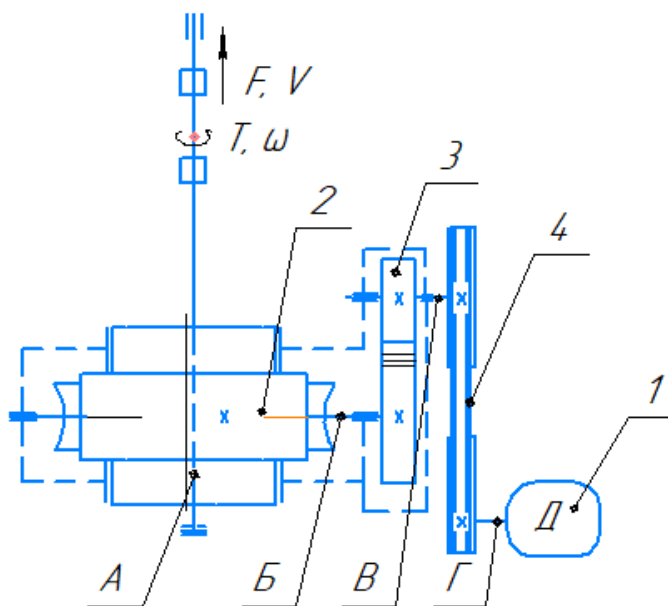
Кінематична схема приводу стрічкового транспортера:
